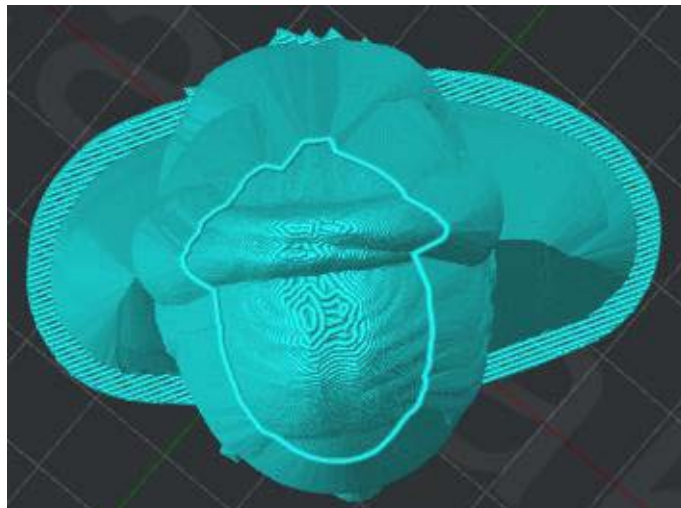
Nastavení úhlu Wipe Wall na 90.
